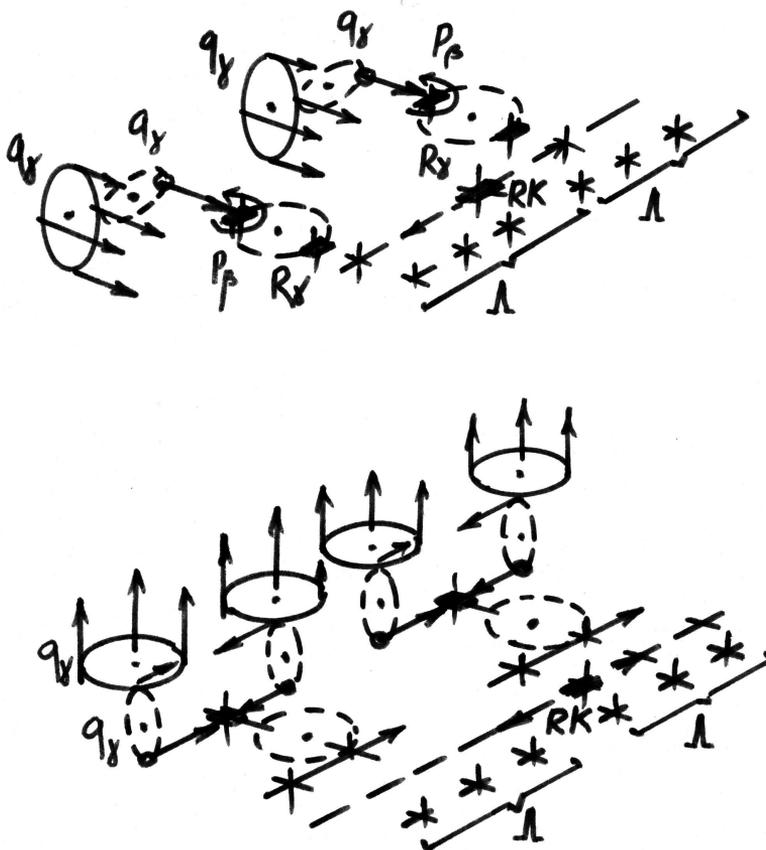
Участки ГПС из модулей для обработки корпусных деталей.
